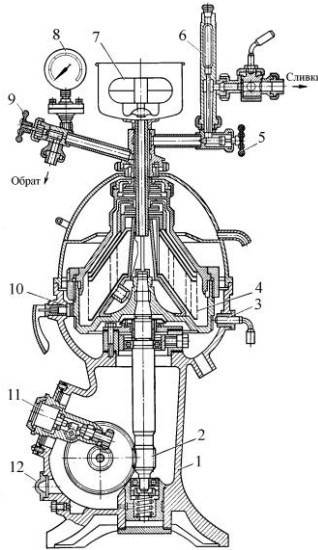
Сепаратор молока Г9-ОСП-3М:1 – станина; 2 – приводной механизм; 3 – стопорный винт; 4 – барабан; 5,9 – вентили; 6 – измеритель сливок; 7 – поплавок; 8 – манометр; 10 – тормоз; 11 – тахометр; 12 – указатель уровня масла
